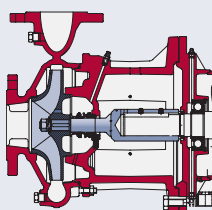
Горизонтальный одноступенчатый консольно-моноблочный насос
